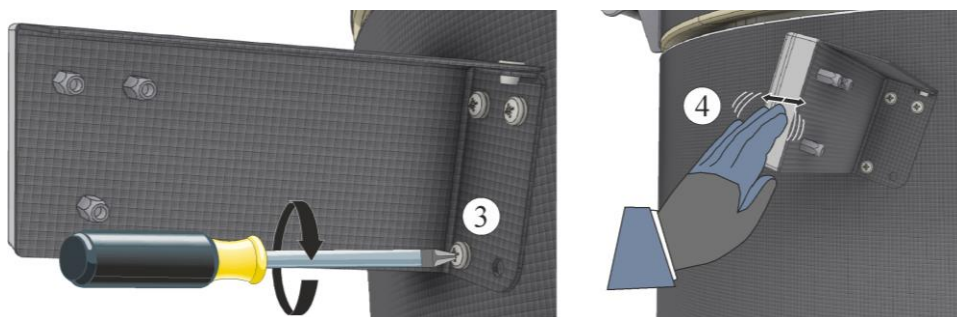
Прочно затяните винты держателя (рисунок примерный)
